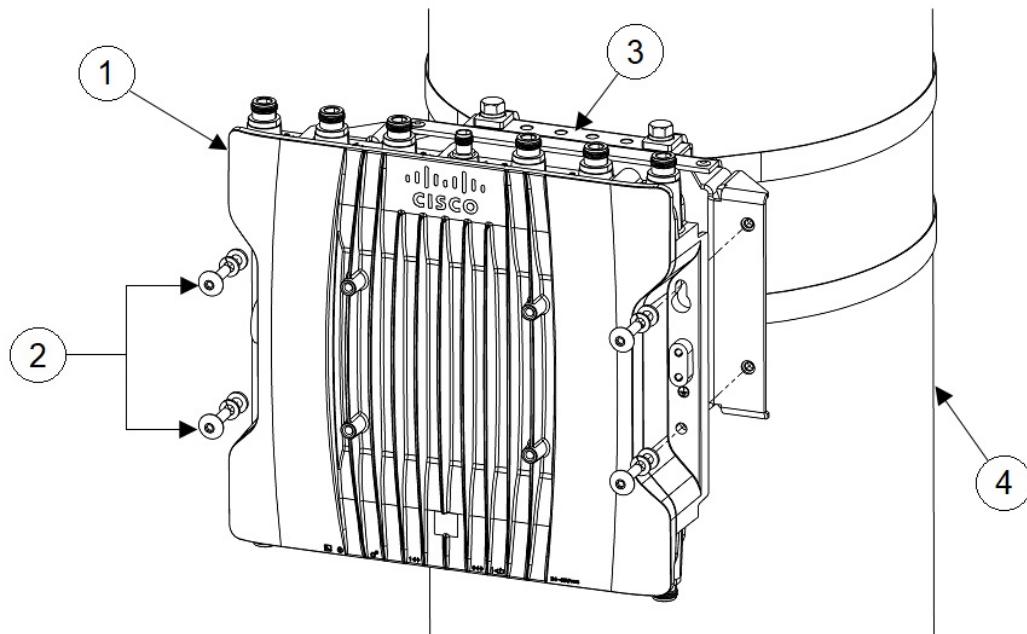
Conjunto de soporte de montaje y abrazadera de fijación para poste
